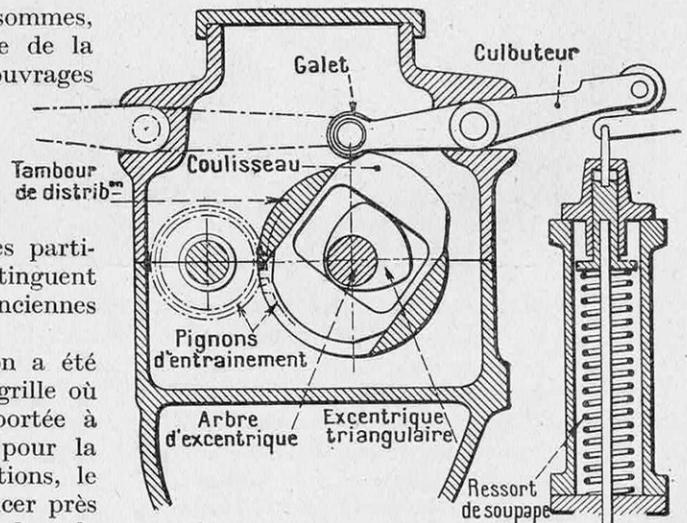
VUE EN COUPE DU DISPOSITIF DE COMMANDE DES SOUPAPES
